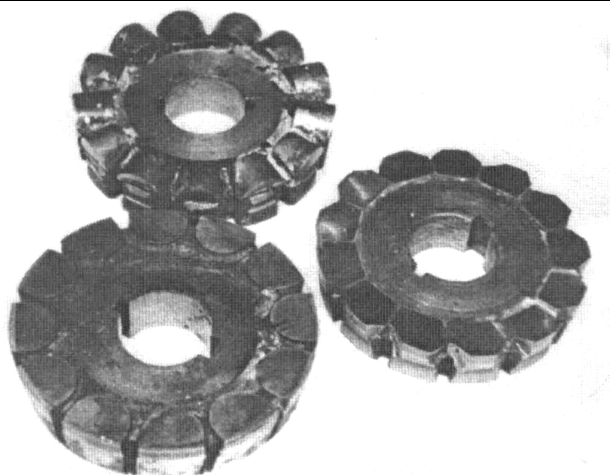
Варианты практического исполнения инструмента с другими различными формами режущих зубьев (в т.ч. и с цилиндрической передней поверхностью)
